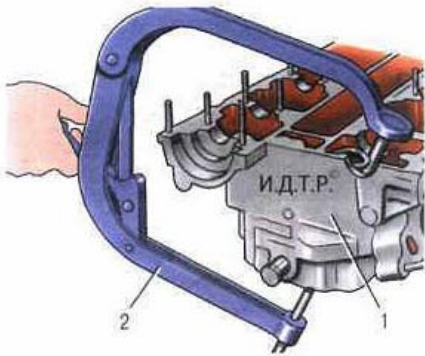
Установка приспособления для сжатия пружин клапанов: 1 - головка блока цилиндров; 2 - приспособление для сжатия пружин
